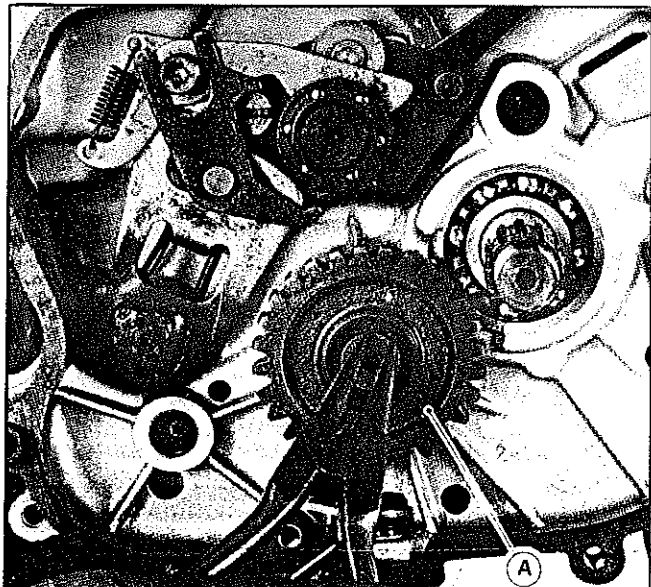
A. ENGRENAGEM INTERM. DO ARRANQUE
